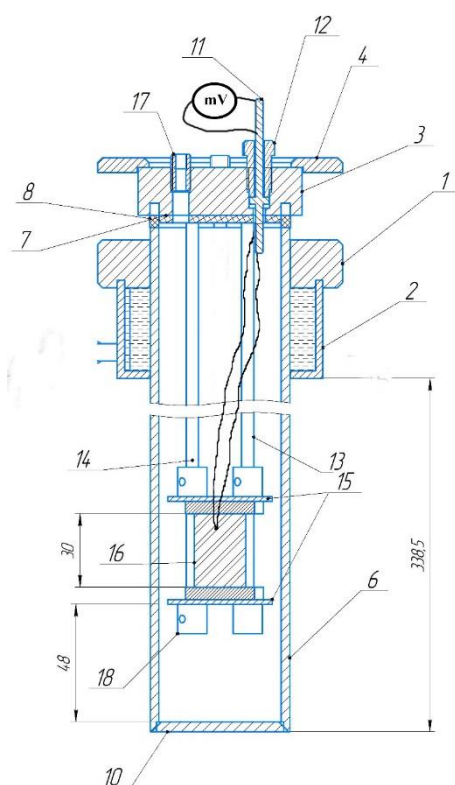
Чертеж установки. 1 – Обечайка; 2 – Кожух охлаждения; 3 – Крышка; 4 – Кольцо; 5 – Перемычка; 6 – Труба; 7 – Термозащита; 8 – Уплотнительная прокладка; 9 – Втулка охлаждения; 10 – Дно; 11 – Токоввод; 12 – Прижимной болт; 13 – Стержни столика; 14 – Газовая трубка; 15 – Планка столика; 16 – Образец; 17 – Переходник для газового ввода; 18 – Втулка.
